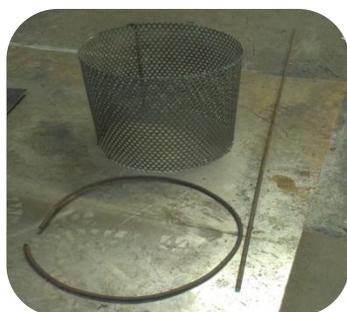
и рисунок 6 – Заготовки для придания жесткости конструкции
